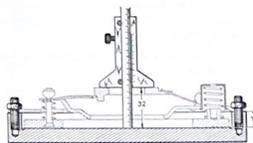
Reglaje del embrague con el montaje simplificado (útil 1703-T).
